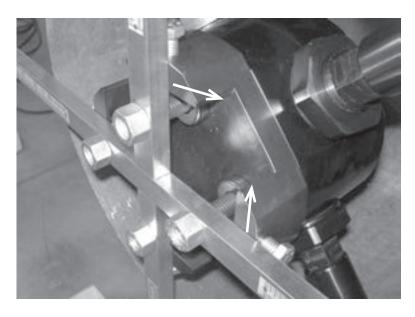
Schrauben Sie die Füße heraus, um den Spanndorn innerhalb des Rohrs zu verspannen.
